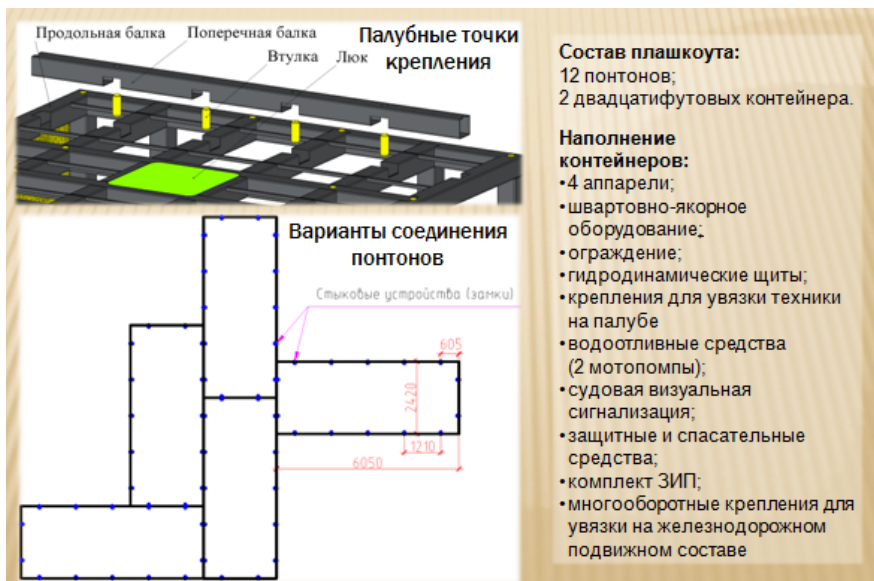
Мобильный палубоут для выполнения строительно-монтажных работ на воде
